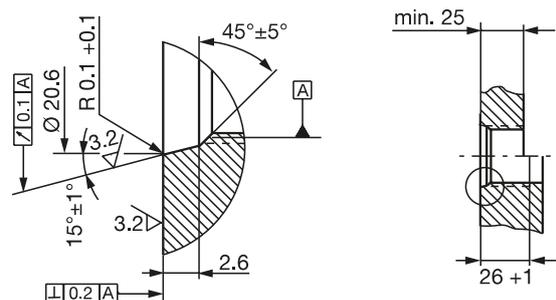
Einschraubloch 3/4"-16UNF nach SAE J475 O-Ring 15.3x2.4
